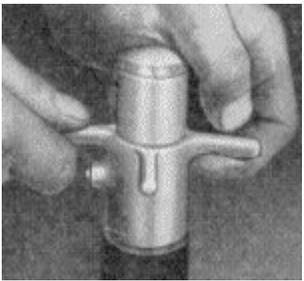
Einsetzen des UG-Dichtringes mit dem Sonderwerkzeug 05 MW 2-3
